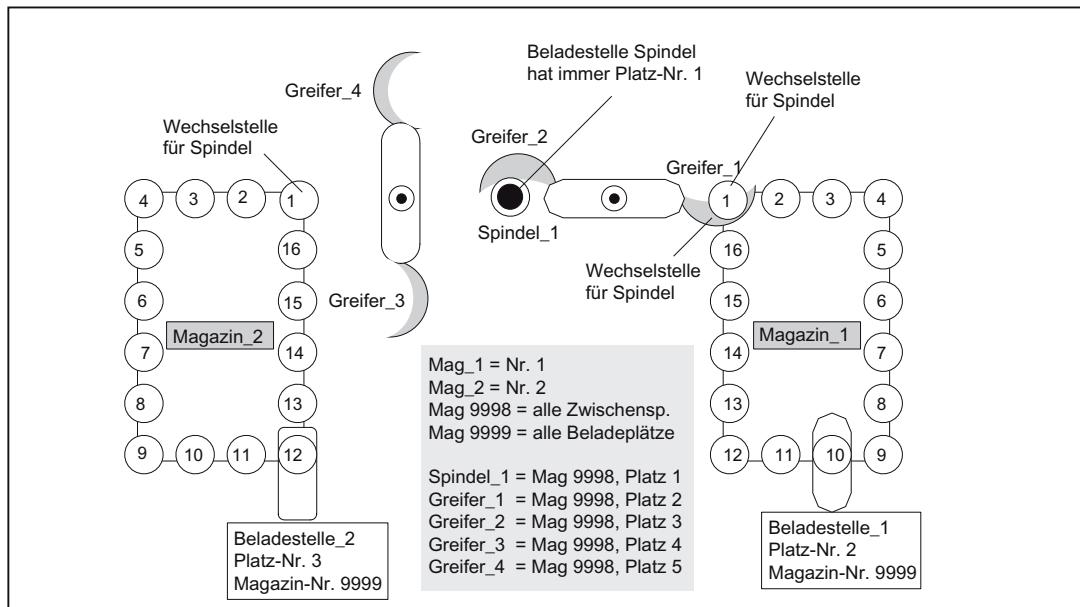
Beispiel einer Maschine mit Zwischenspeicher und Belademagazin
